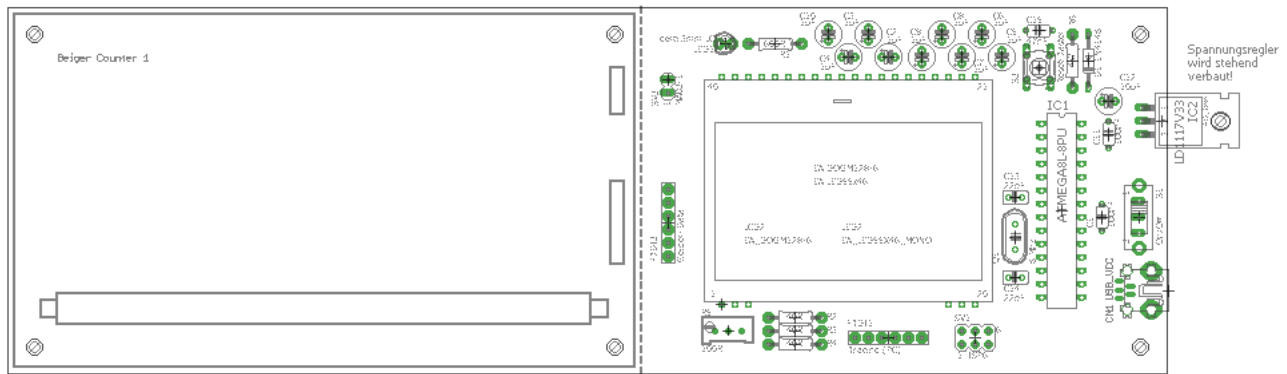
PCB myGeigerle – Bestückung Top Layer
